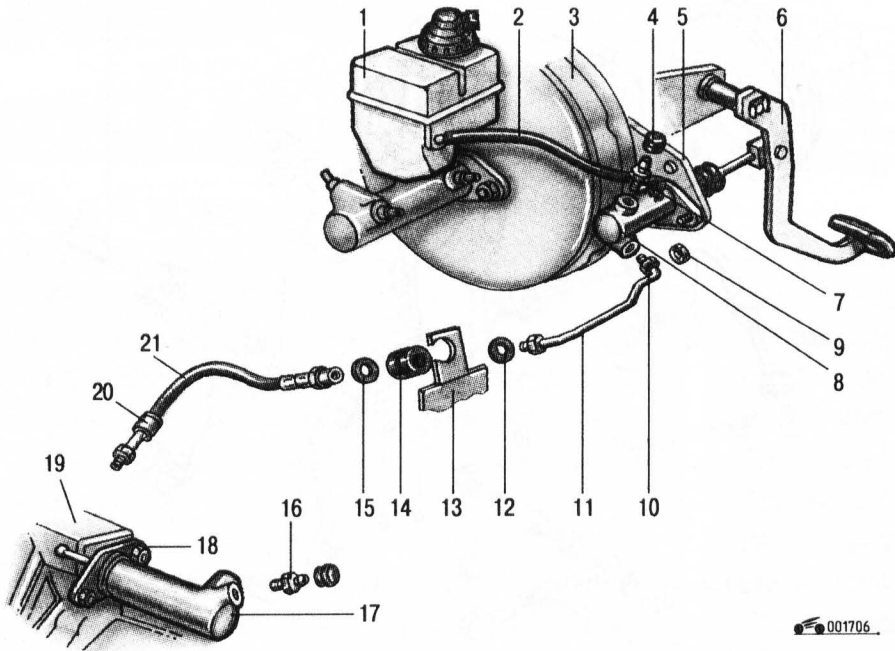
Элементы гидравлического привода выключения сцепления: 1 – бачок главного тормозного цилиндра/гидравлического привода выключения сцепления; 2 – шланг подачи жидкости; 3 – вакуумный усилитель тормозов; 4 – защитный колпачок; 5 – кронштейн сервопривода тормозов; 6 – педаль сцепления; 7 – штуцер прокачки главного цилиндра сцепления; 8 – главный цилиндр сцепления; 9 – гайка крепления кронштейна главного цилиндра сцепления; 10 – муфта трубопровода; 11 – трубопровод; 12 – прокладка; 13 – опора; 14 – втулка; 15 – прокладка; 16 – штуцер прокачки рабочего цилиндра сцепления; 17 – рабочий цилиндр сцепления; 18 – гайка крепления рабочего цилиндра; 19 – картер сцепления; 20 – муфта гибкого шланга; 21 – гибкий шланг
